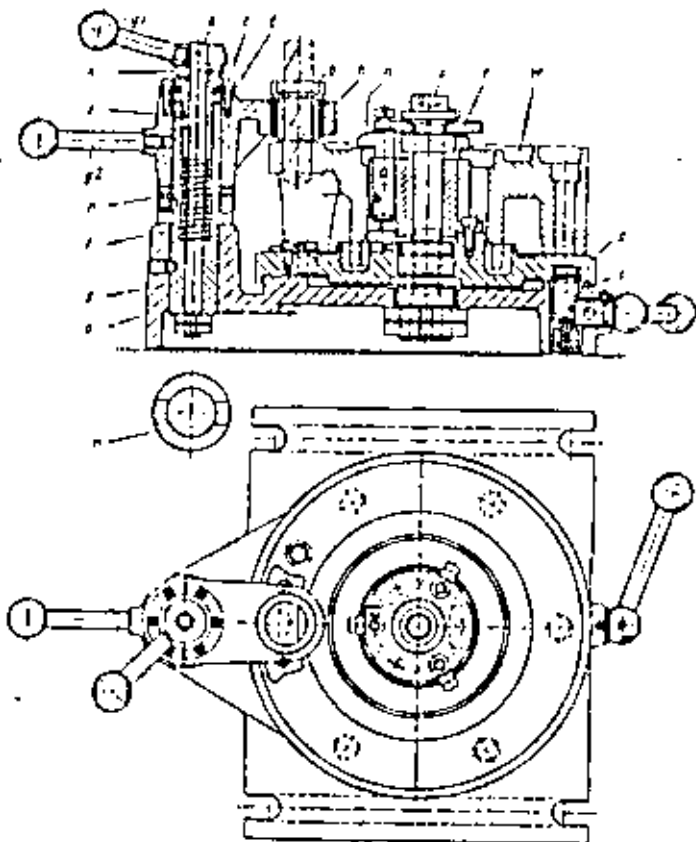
Dispositivo de taladrado con soporte de casquillo de taladrar que puede girar.
